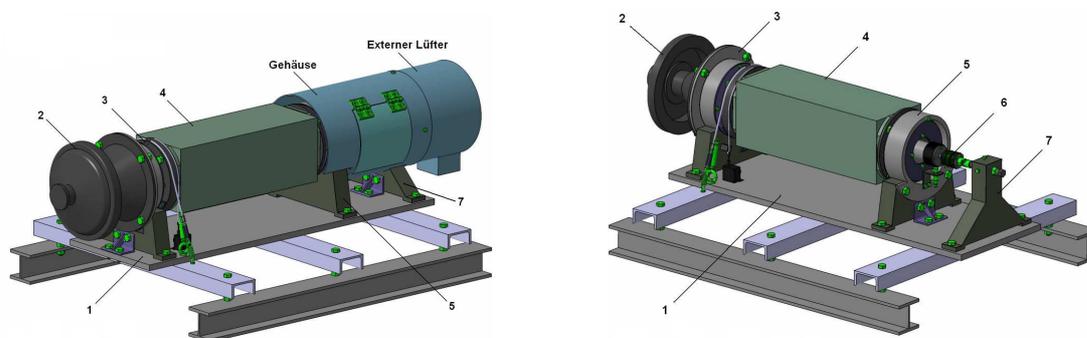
Aufbau der Motoraufhängung - *kvp-003-00-00
